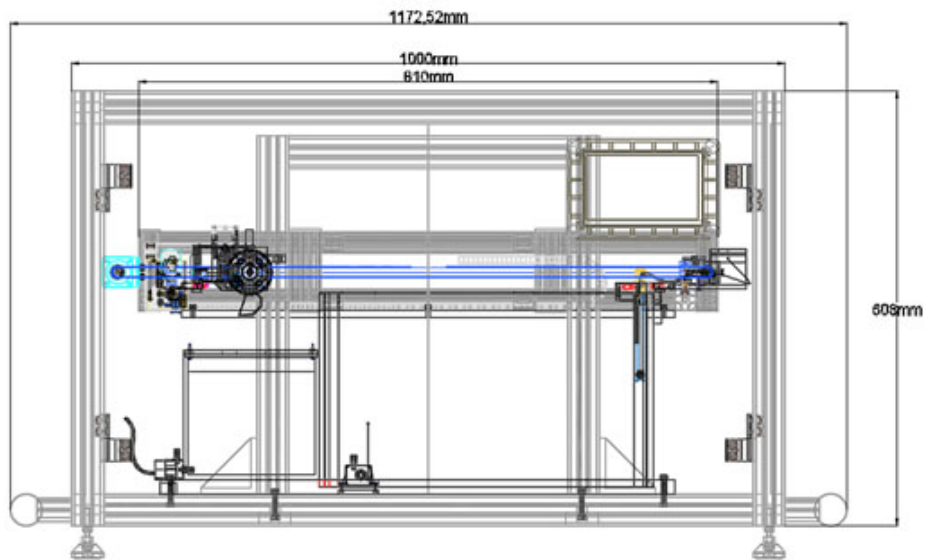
Alzado longitudinal con las dimensiones del domo. Elaboración propia.
